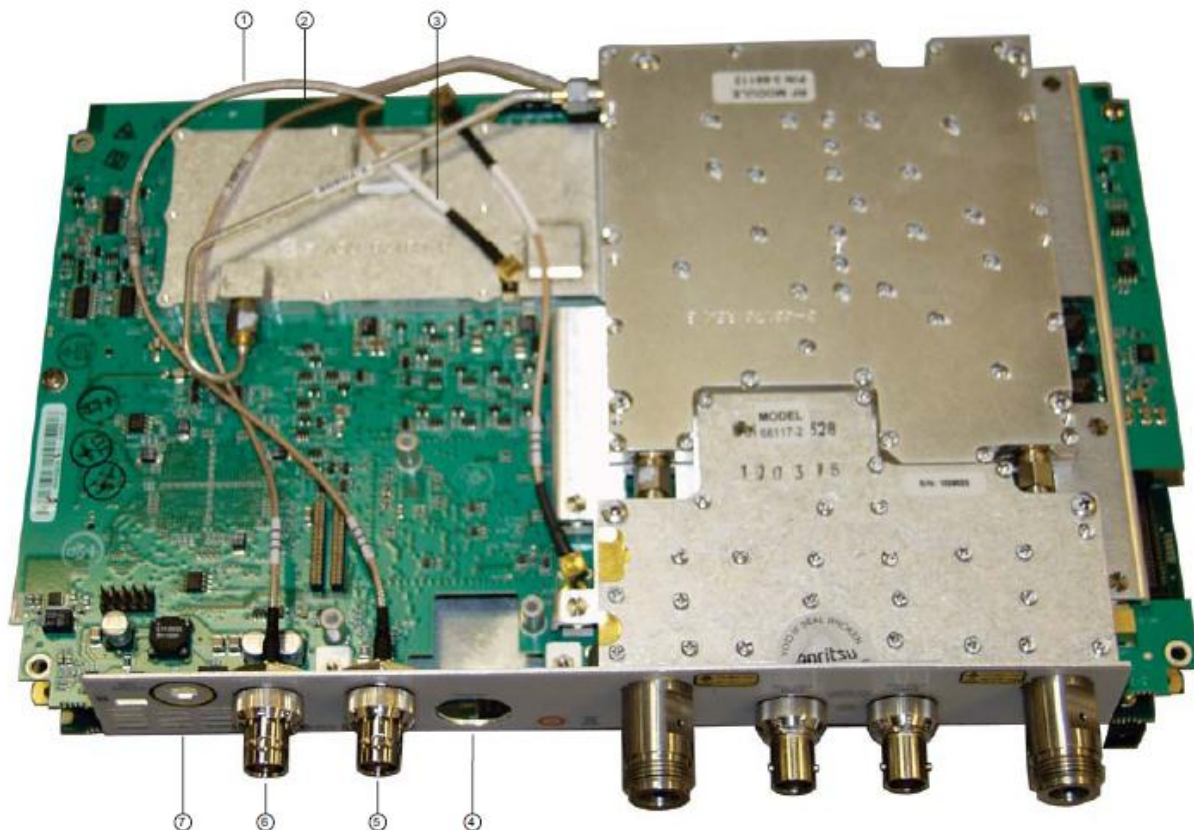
Umieszczenie wkrętów zespołu PCB VNA
